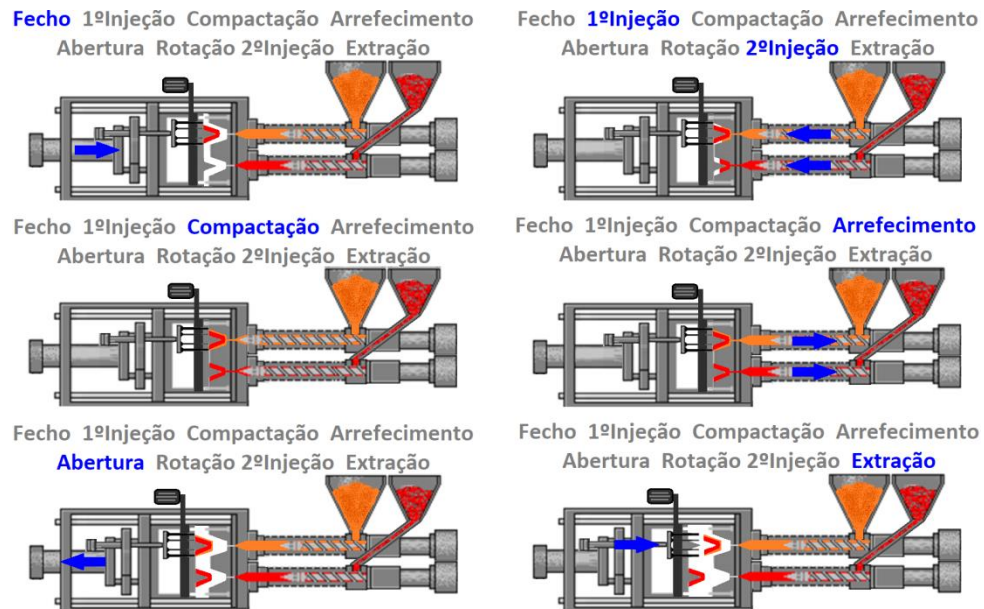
Processo de Moldagem por Injeção (2) (Adaptada de [9])
